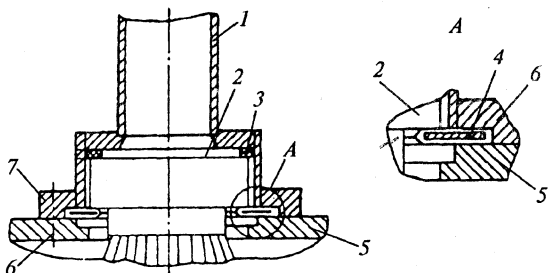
Узел крепления трубных решеток погружного фторопластового теплообменника к корпусу аппарата: 1 — штуцер; 2 — трубная решетка; 3 — резиновое кольцо; 4 — плоская резиновая прокладка во фторопластовом чехле; 5 — корпус аппарата; 6 — болтовое соединение; 7 — крышка аппарата
